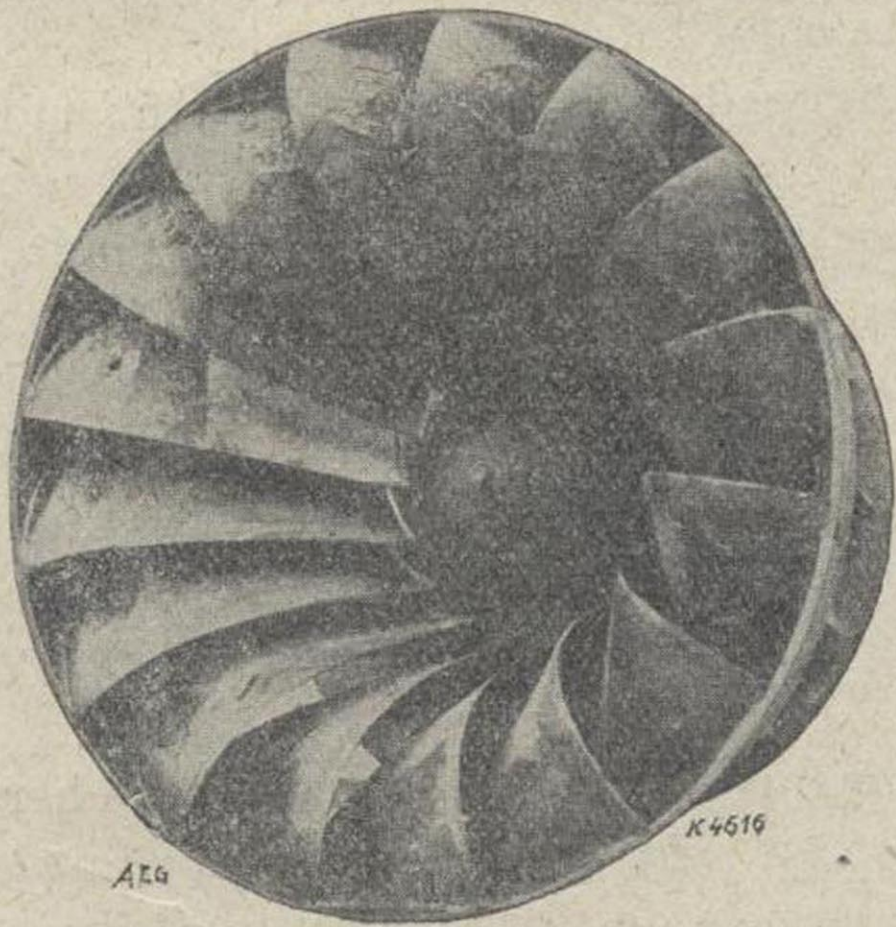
Rueda de turbina hidráulica soldada por arco.
